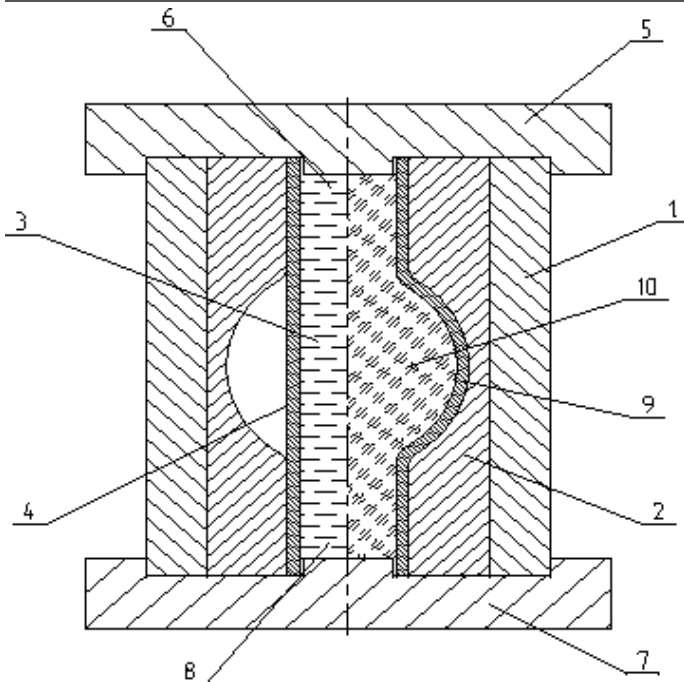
Штмп для раздачи тонкостенной трубной заготовки
